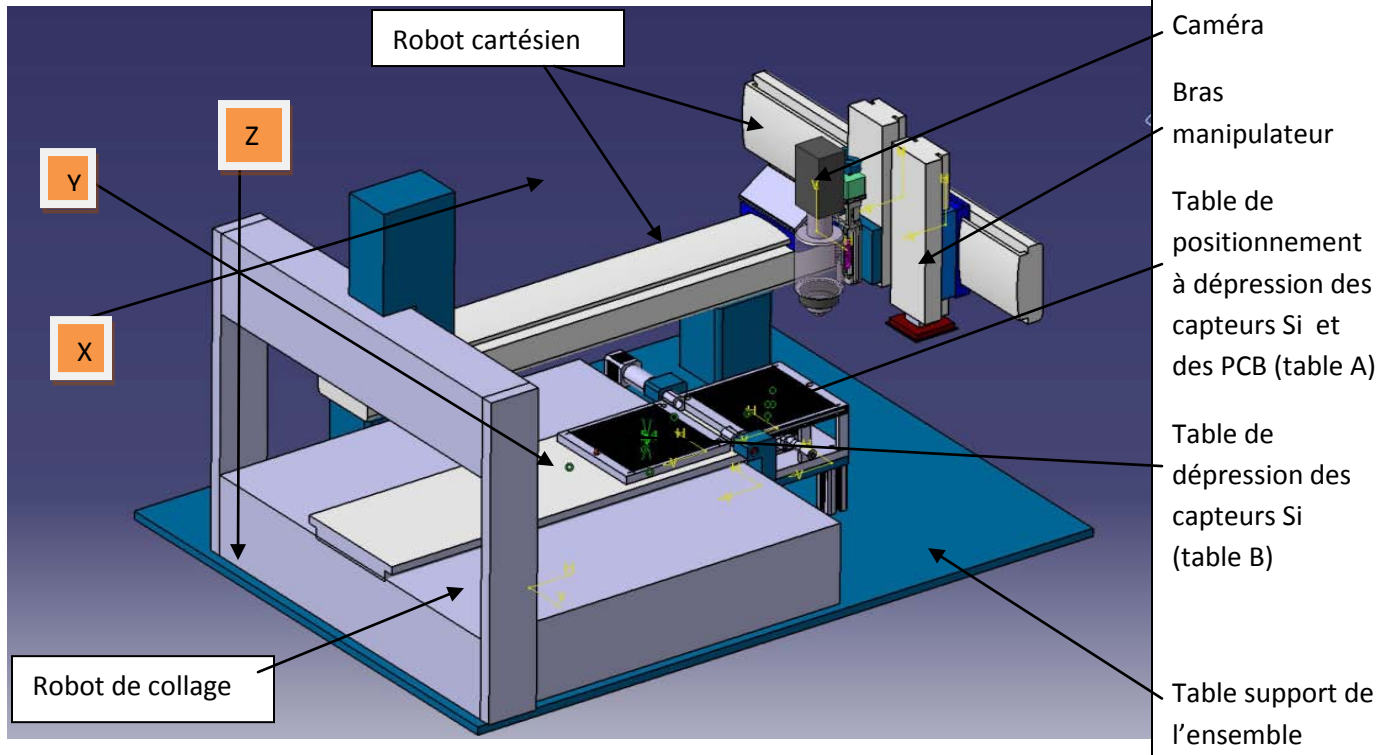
outillage pour le collage des capteurs Si sur PCB
